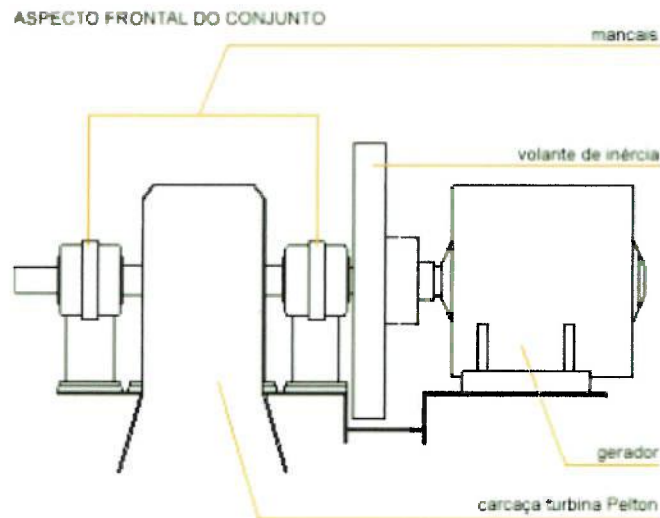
Conjunto Turbina Pelton e Gerador. [5]
